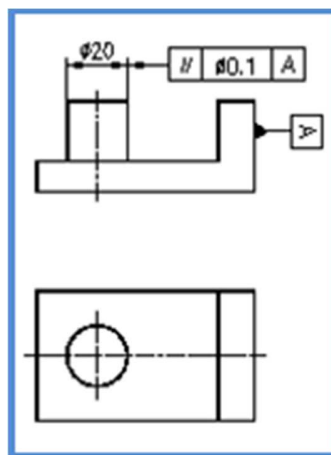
Ejemplo de rectángulo de tolerancias geométricas
